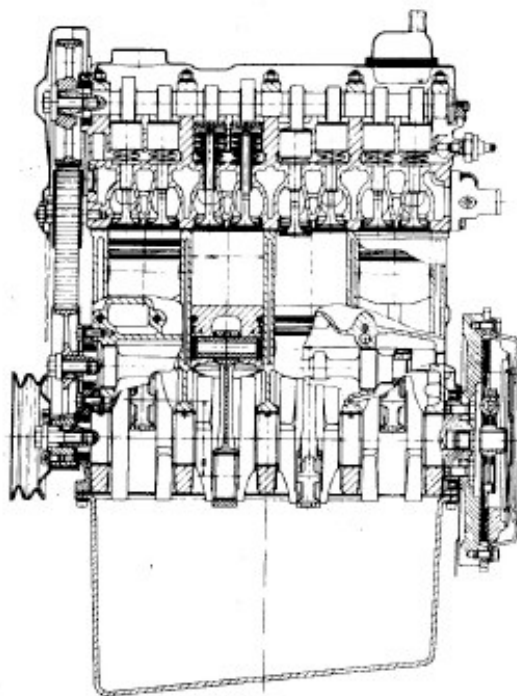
Wassergekühlter Vierzylinder-Dieselmotor für den VW-Transporter
